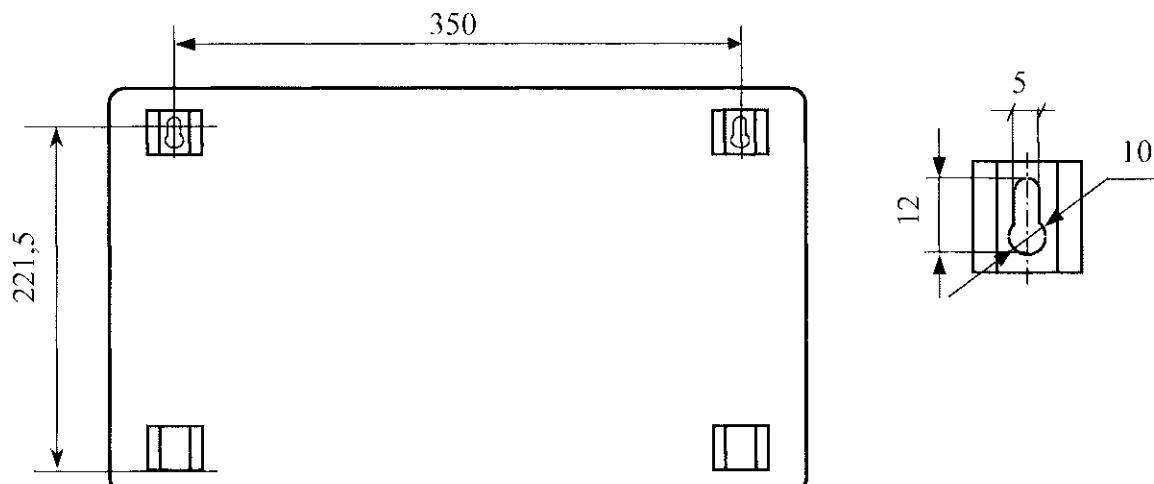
Установочные, присоединительные размеры (вид сзади)
